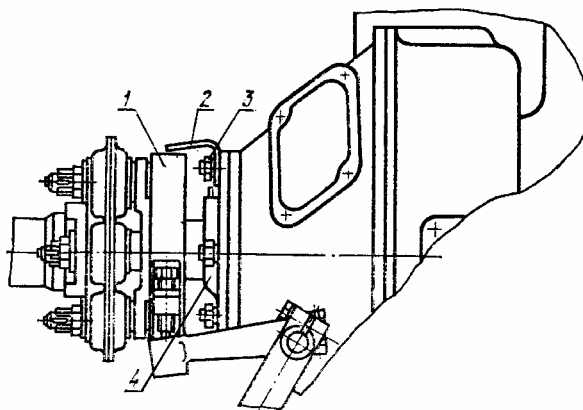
Установка стрелки для проверки угла опережения подачи топлива:
